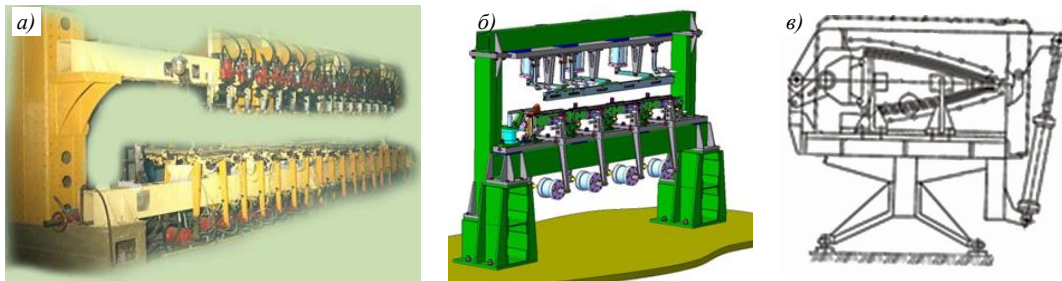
Вид стапеля (а) и компьютерная модель секции стапеля (б) общей сборки лопасти несущего винта, а также сборочно-клеечное приспособление для склейки хвостового отсека (в)
